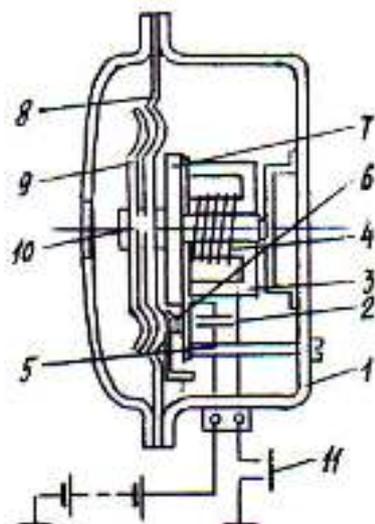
Звуковой сигнал: 1 – корпус; 2 – конденсатор; 3 – сердечник; 4 – магнит с обмотками; 5 – регулировочный винт; 6 – прерыватель; 7 – якорь; 8 – мембрана; 9 – резонатор; 10 – центральный винт; 11 – кнопка
